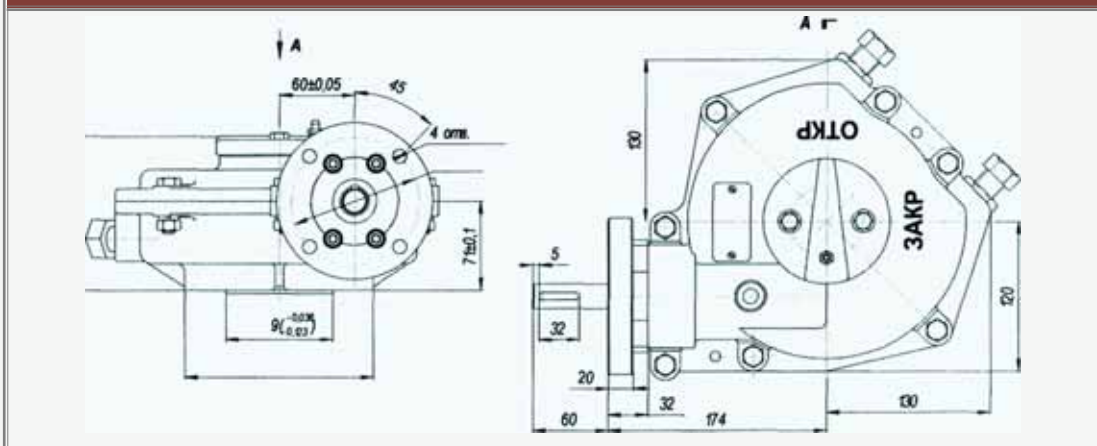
Общий вид спирoидного редуктора PC1-60-В с винтовым ограничителем поворота червяка
